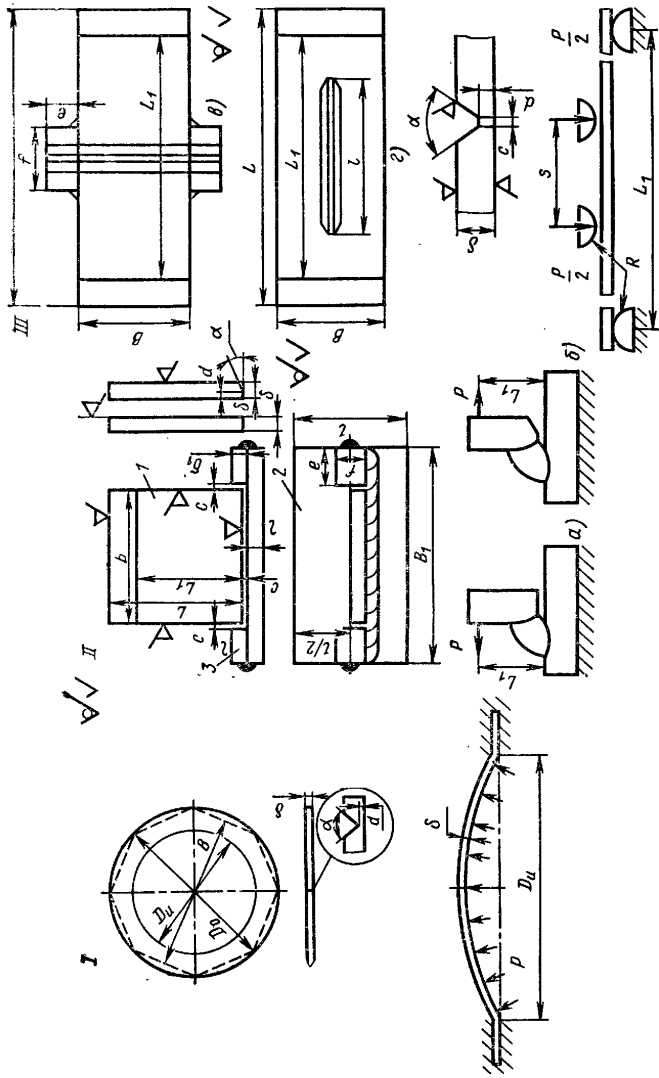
Форма, размеры образцов и схемы их испытаний по методу ЛТП2: I — круглый (восьмигранный) образец; II — газорезный образец для испытаний околошовной зоны (a) и сварного шва (б); I — стенка из испытываемой стали; 2 и 3 — планка из стали Ст3; III — стыковой образец с поперечным (б) и продольным (в) швами;
